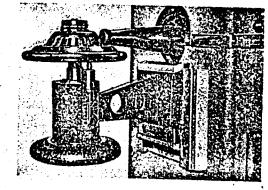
Приспособление для ультразвуковой сварки малых металлокерамических контантов.
